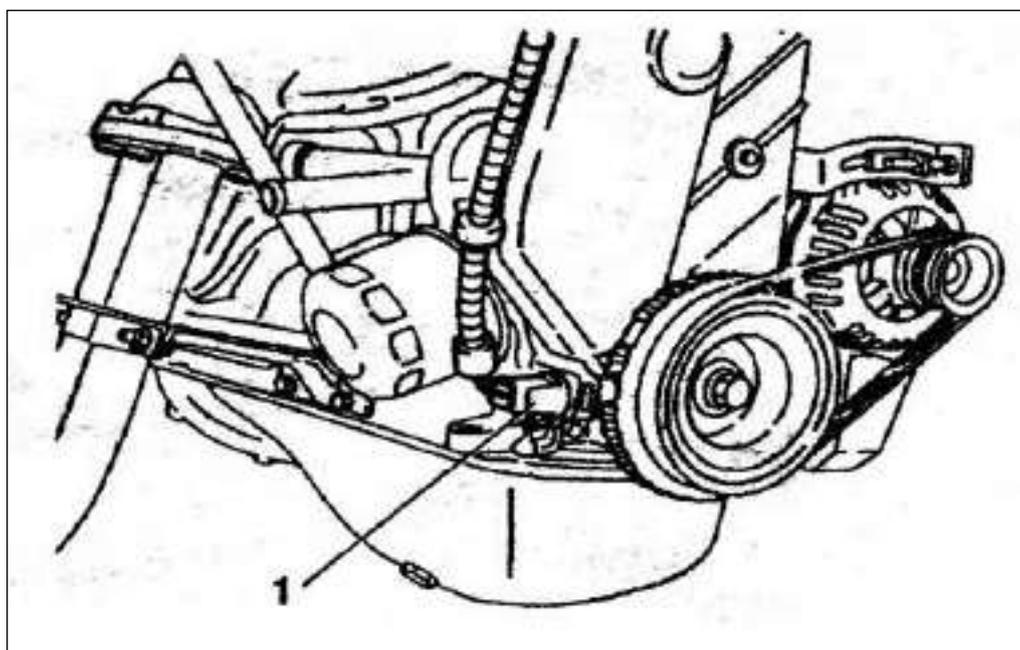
Размещение датчика положения коленчатого вала (1) на двигателе:
